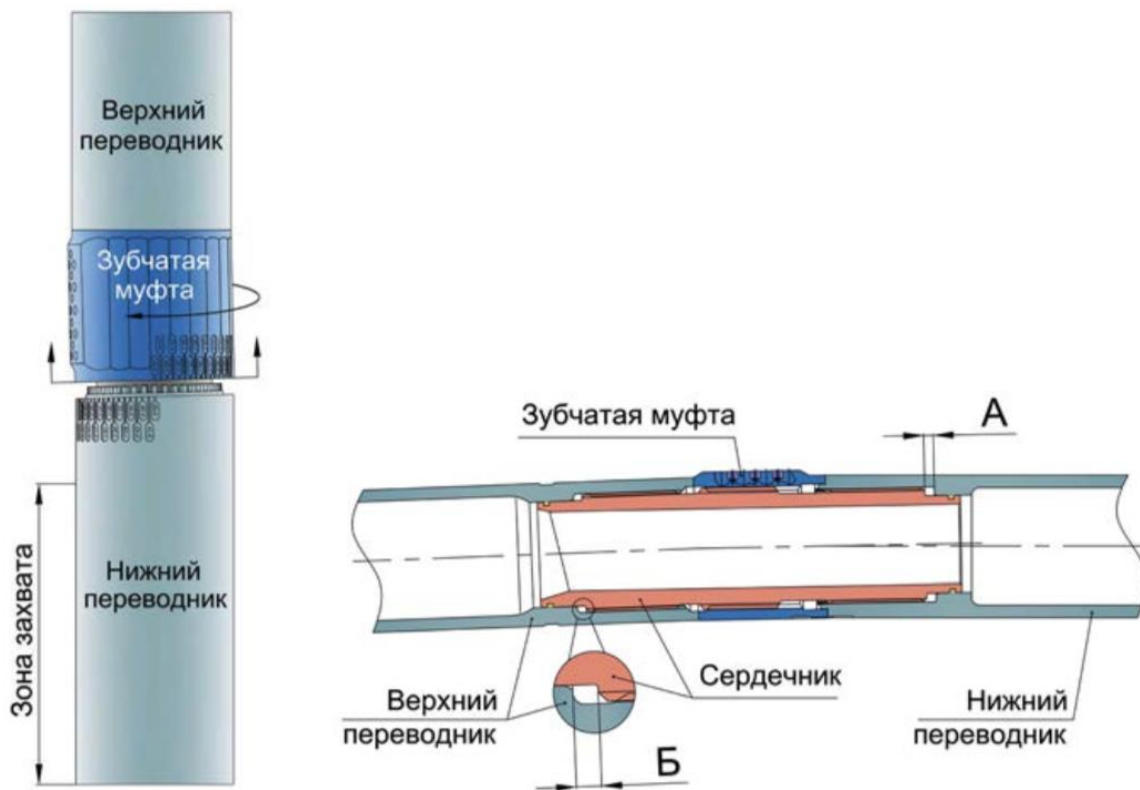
Регулятор угла винтового забойного двигателя
